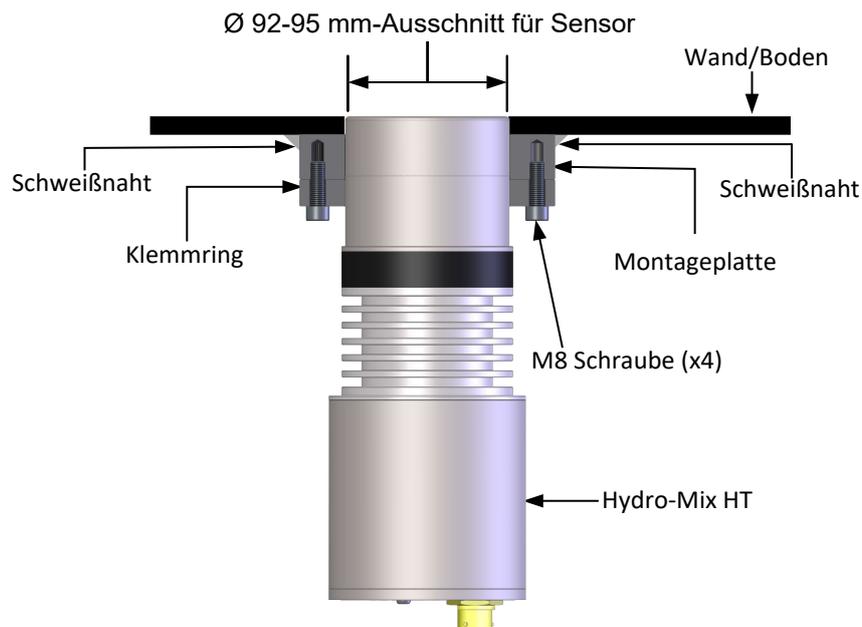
Einbau des Sensors (Extern montierte Montageplatte)
